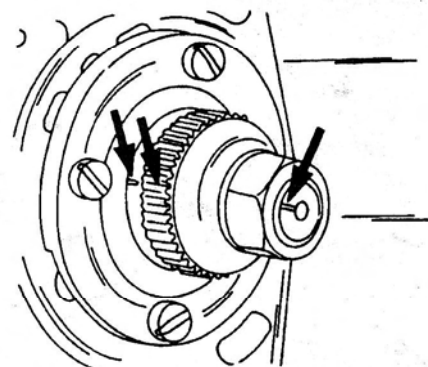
При надевании новой поводковой шестерни указанные стрелками метки должны совпадать.
